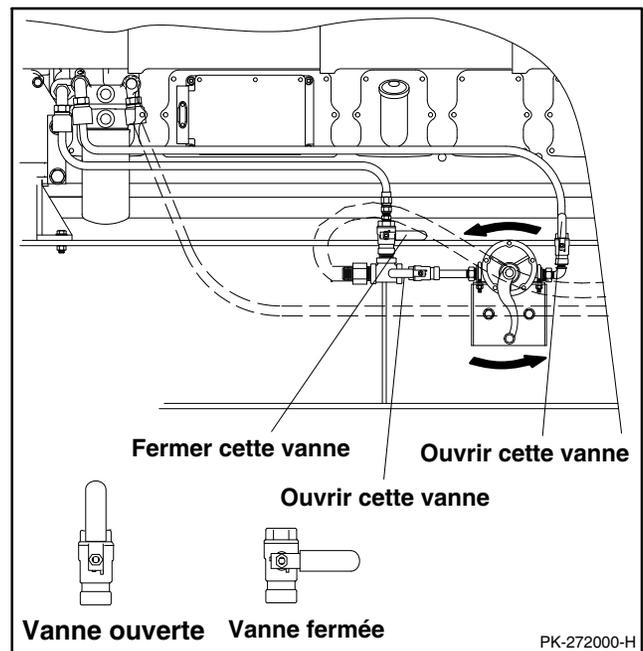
Pompe d'amorçage manuelle avec positions de vannes pour l'amorçage de carburant (groupe électrogène sans préfiltre à carburant illustré), Typique
